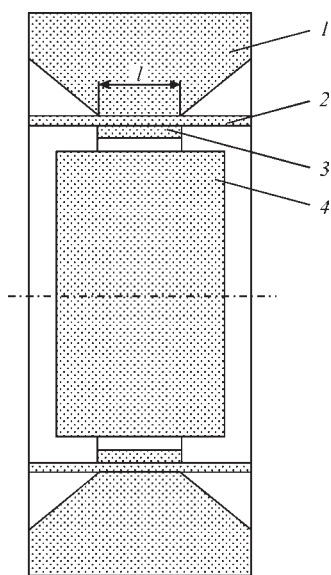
Схема одновиткового індуктора з заготовками перед зварюванням: 1 – індуктор; 2 – ізолятор; 3 – мідне кільце; 4 – сталеві заготовки-мішені
